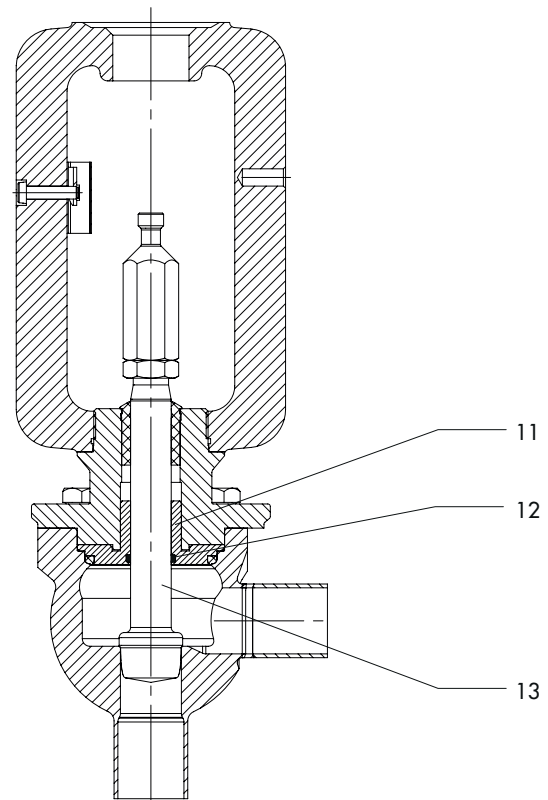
Ventil Typ 3347, Gehäuse in Gussausführung
